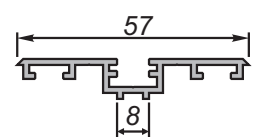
Алюминиевый универсальный профиль. Вид в разрезе.
